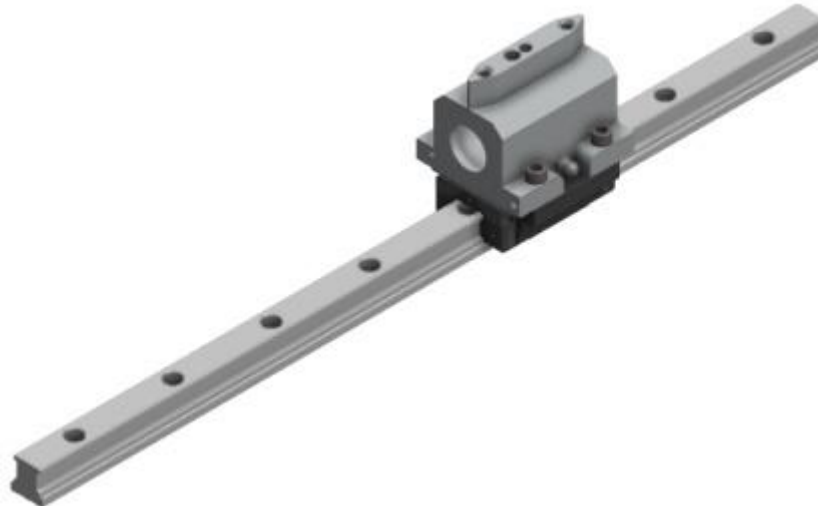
Stahlwellenführung CPC20 mit Führungsschlitten
